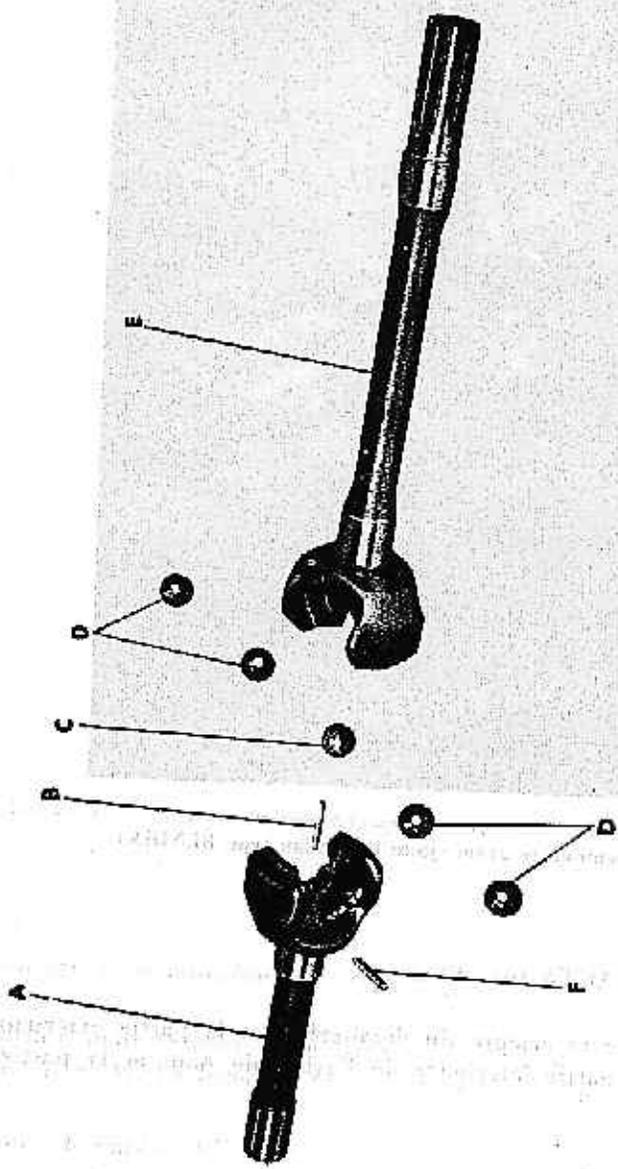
Demi-arbre avant, Vue éclatée (Joint de cardan type BENDIX)
